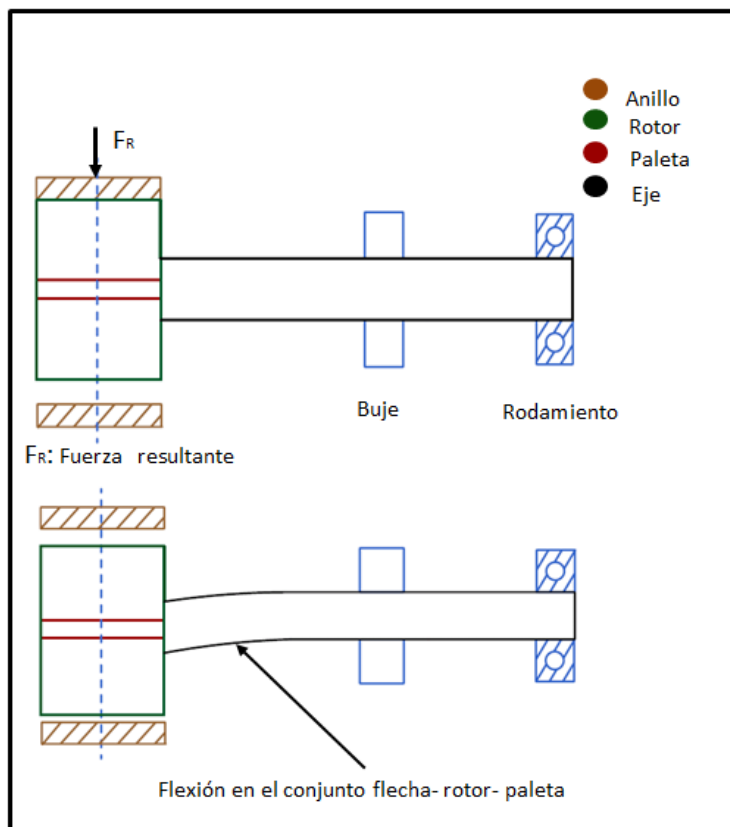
Cabeceo del conjunto flecha-rotor-paleta, con apoyos en un extremo.
